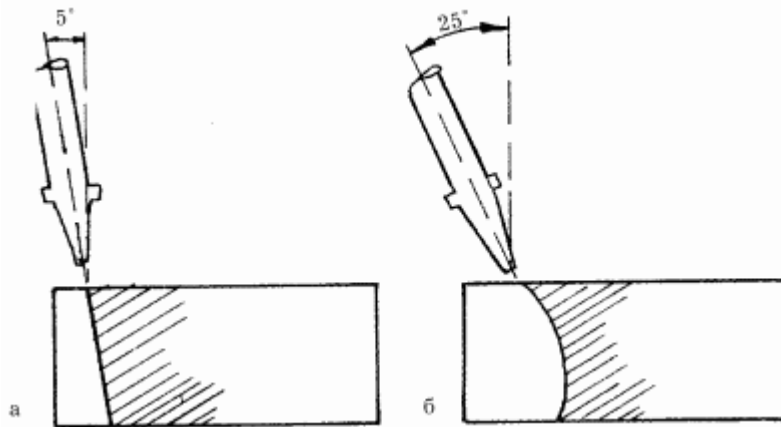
Положение резака при работе с листовой сталью: а – начало резки; б – процесс резки.
